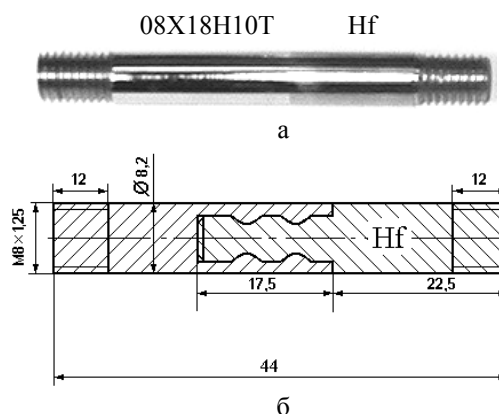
Образец соединения гафний–нержавеющая сталь для стержневых комбинированных пэлов: а – внешний вид образца; б – конструкция образца
